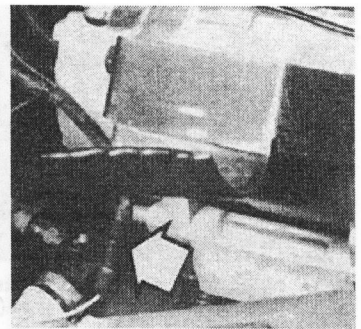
Отсоедините электрический разъем крепления компрессора (указан стрелкой) — двигатель с 6 цилиндрами в линию.
